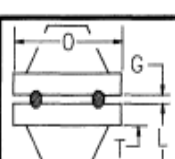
Simbología de tipo de conexión Butt welding
